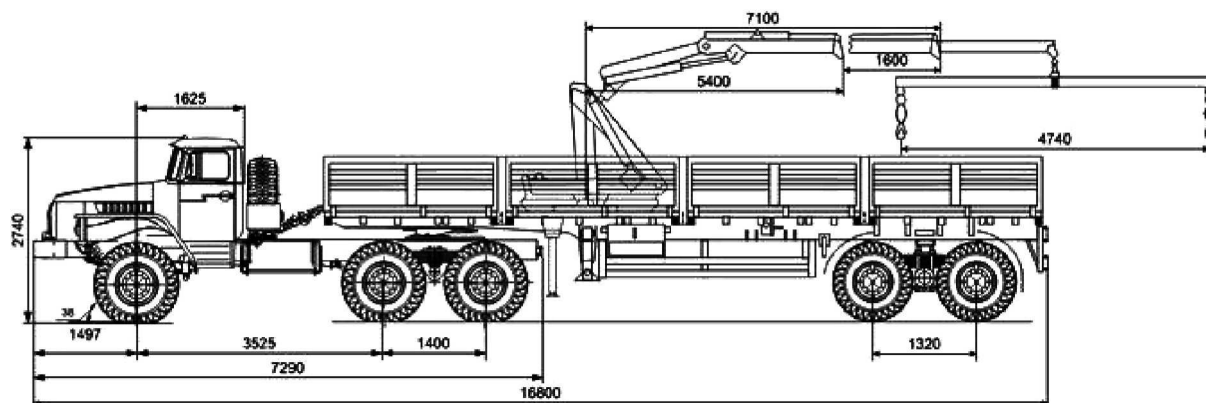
Агрегат перевозки штанг АПШ-89 на базе тягача Урал-44202
